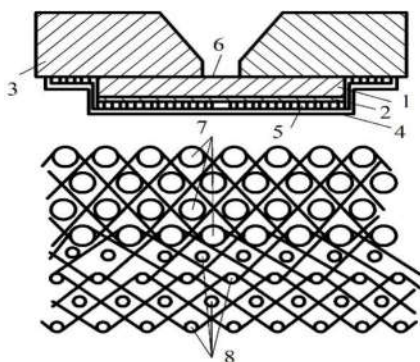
Схема устройства и расположения подкладной ленты (с расшифровкой позиций):
